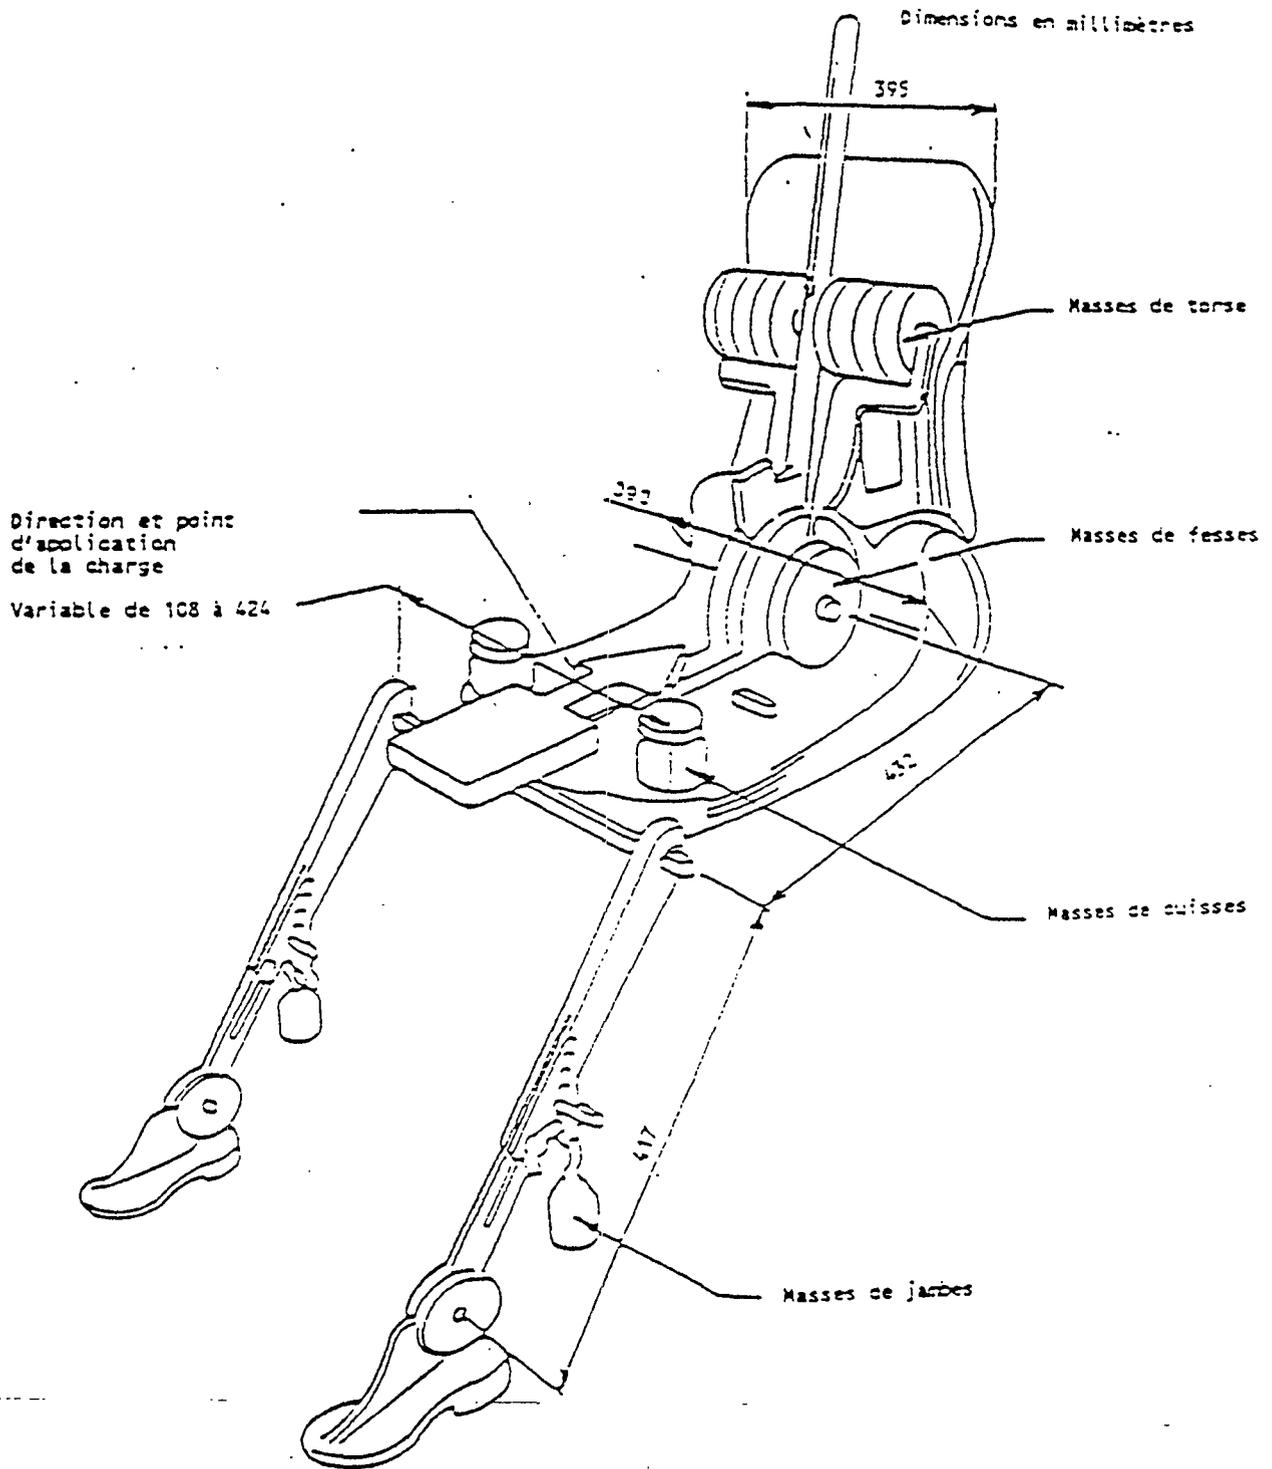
Dimensions des éléments de la machine 3-D H et emplacement des masses
